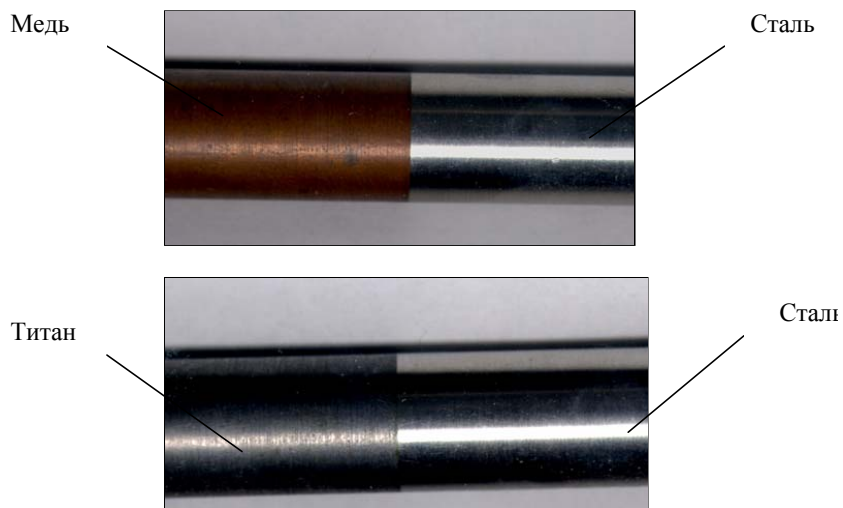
Сварные соединения, выполненные диффузионной сваркой
